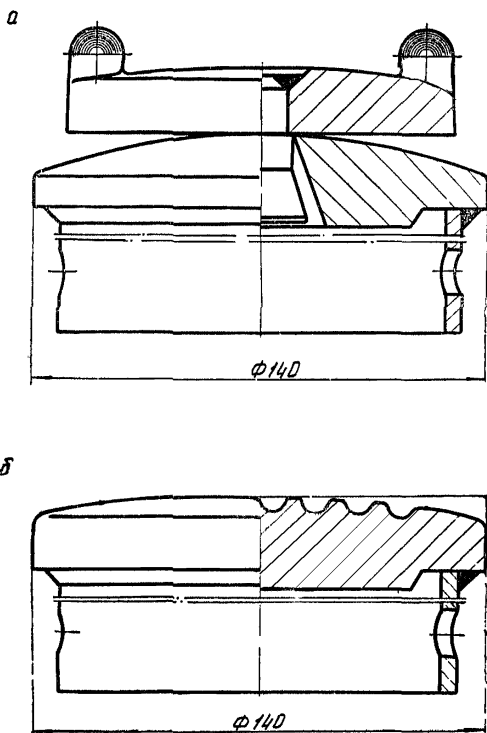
Насадки стоек ГС для работы с металлическими и деревянными верхняками
